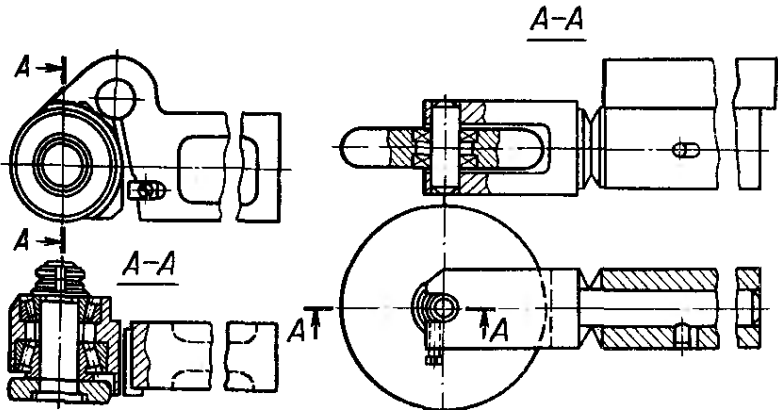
Інструмент для обкочування зовнішніх циліндричних поверхонь
